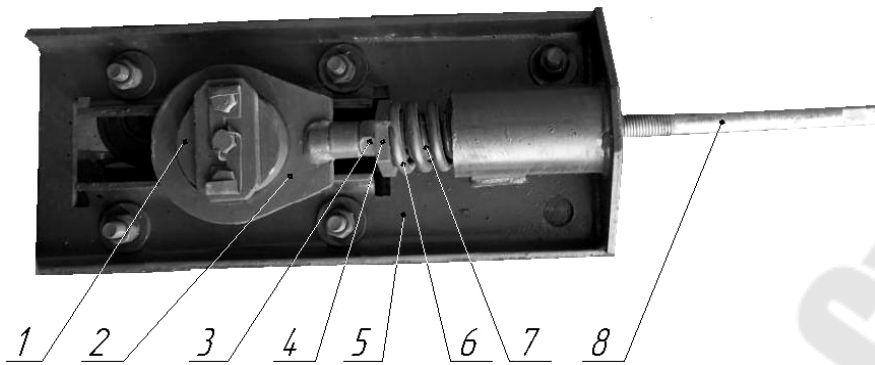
Схема регулировки натяжения механизма прессования: 1 – ось прессующего механизма; 2 – серьга со вставкой; 3 – гайка М16; 4 – гайка; 5 – основание; 6, 7 – пружины; 8 – шпилька
